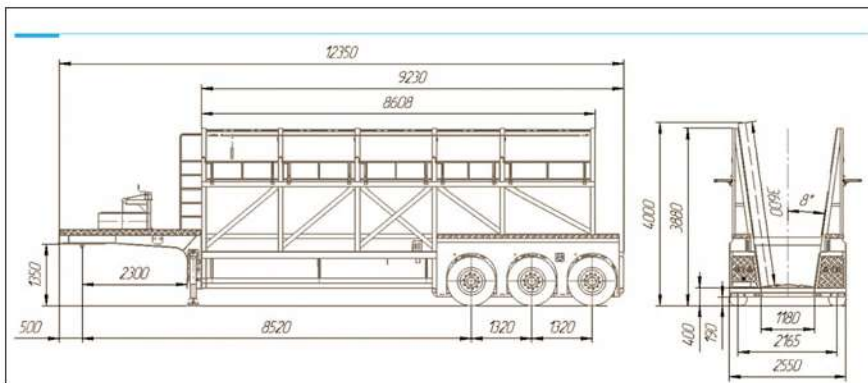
Пример полуприцепа для перевозки стеновых железобетонных панелей
